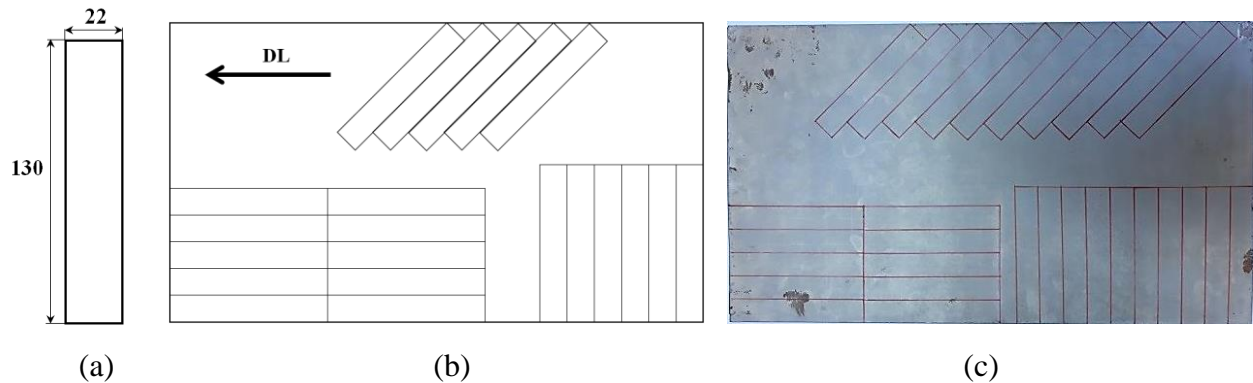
Traçage des éprouvettes à découper sur la tôle.
